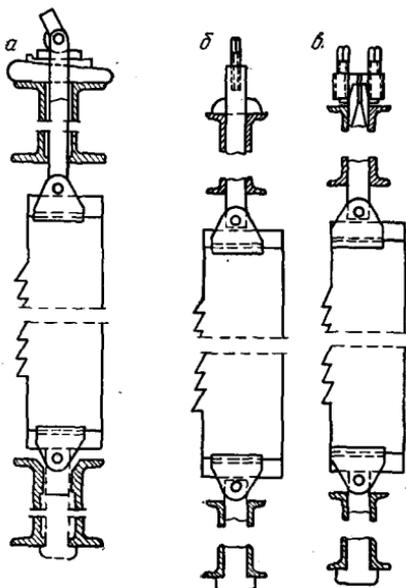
Карабины для укрепления и натяжения пил в пильной рамке: а — эксцентриковый; б — винтовой одно-рядный; в — винтовой шахматный
